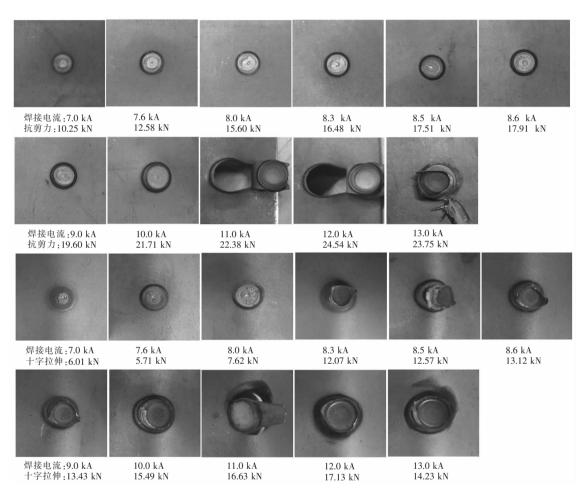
点焊接头力学性能及失效模式 Fig.3 Mechanical properties and failure cause of weld joints
